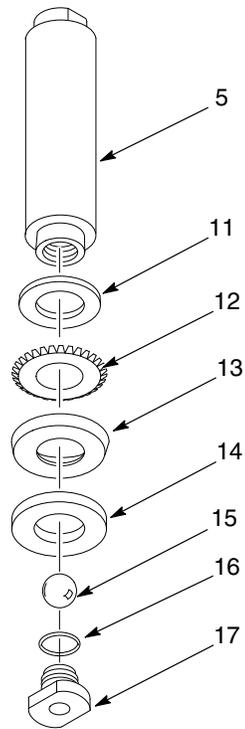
Reparieren der Baugruppe Tauchkolben
